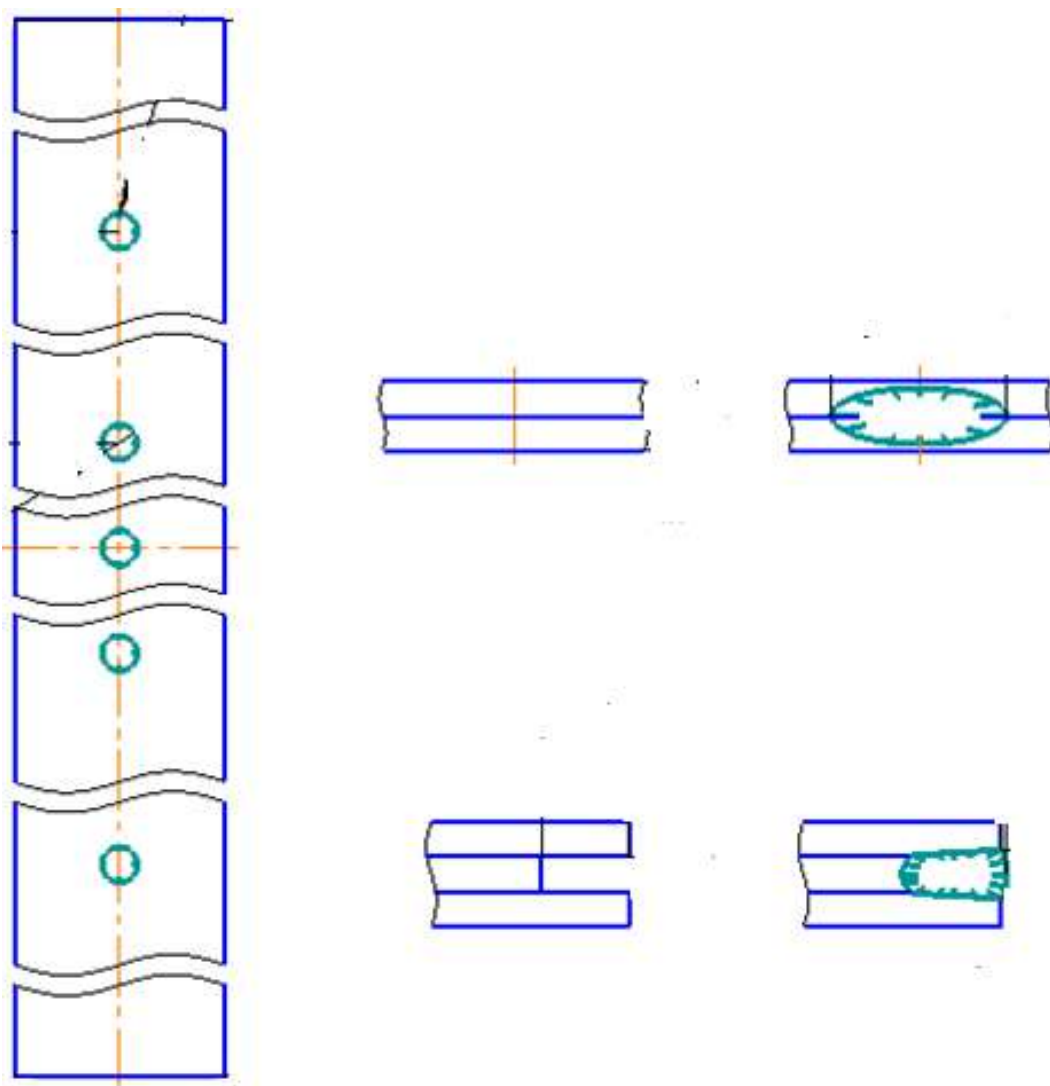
Спосіб контактеного зварювання пластин
